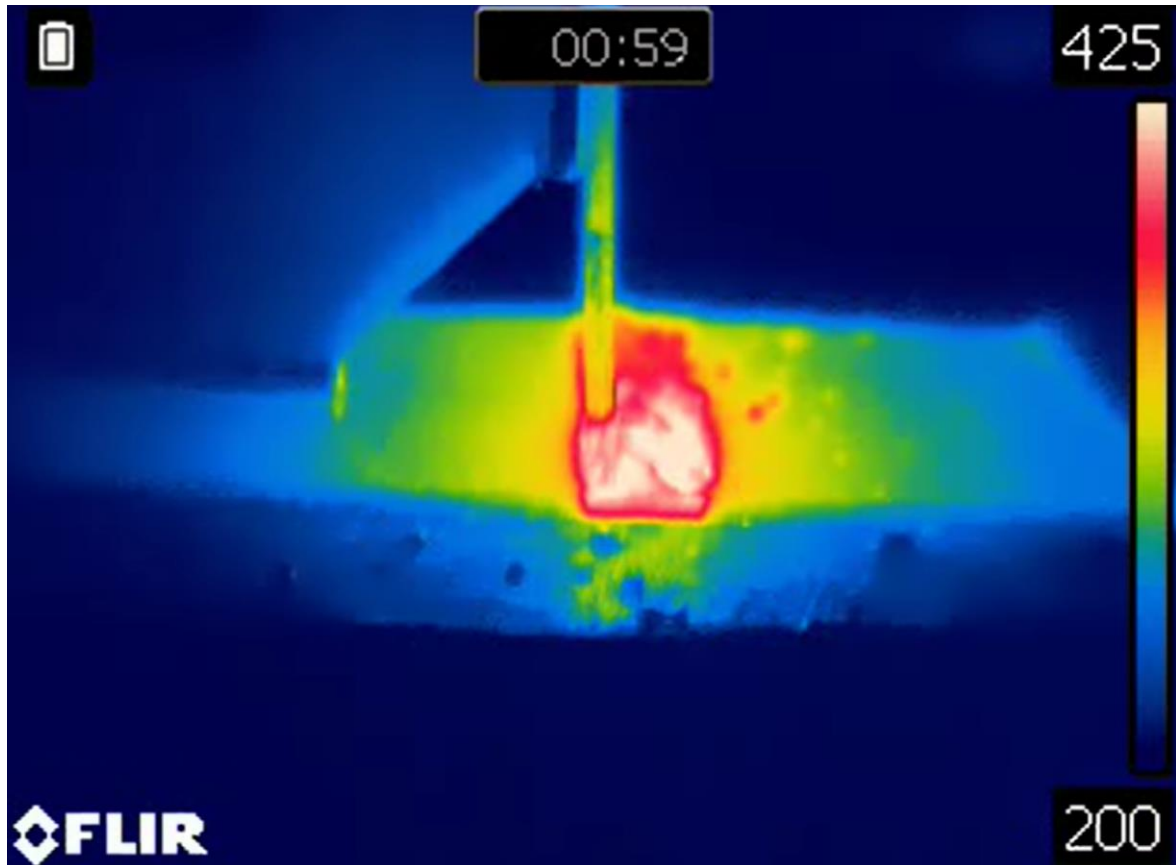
Montaje para la soldadura MIG
